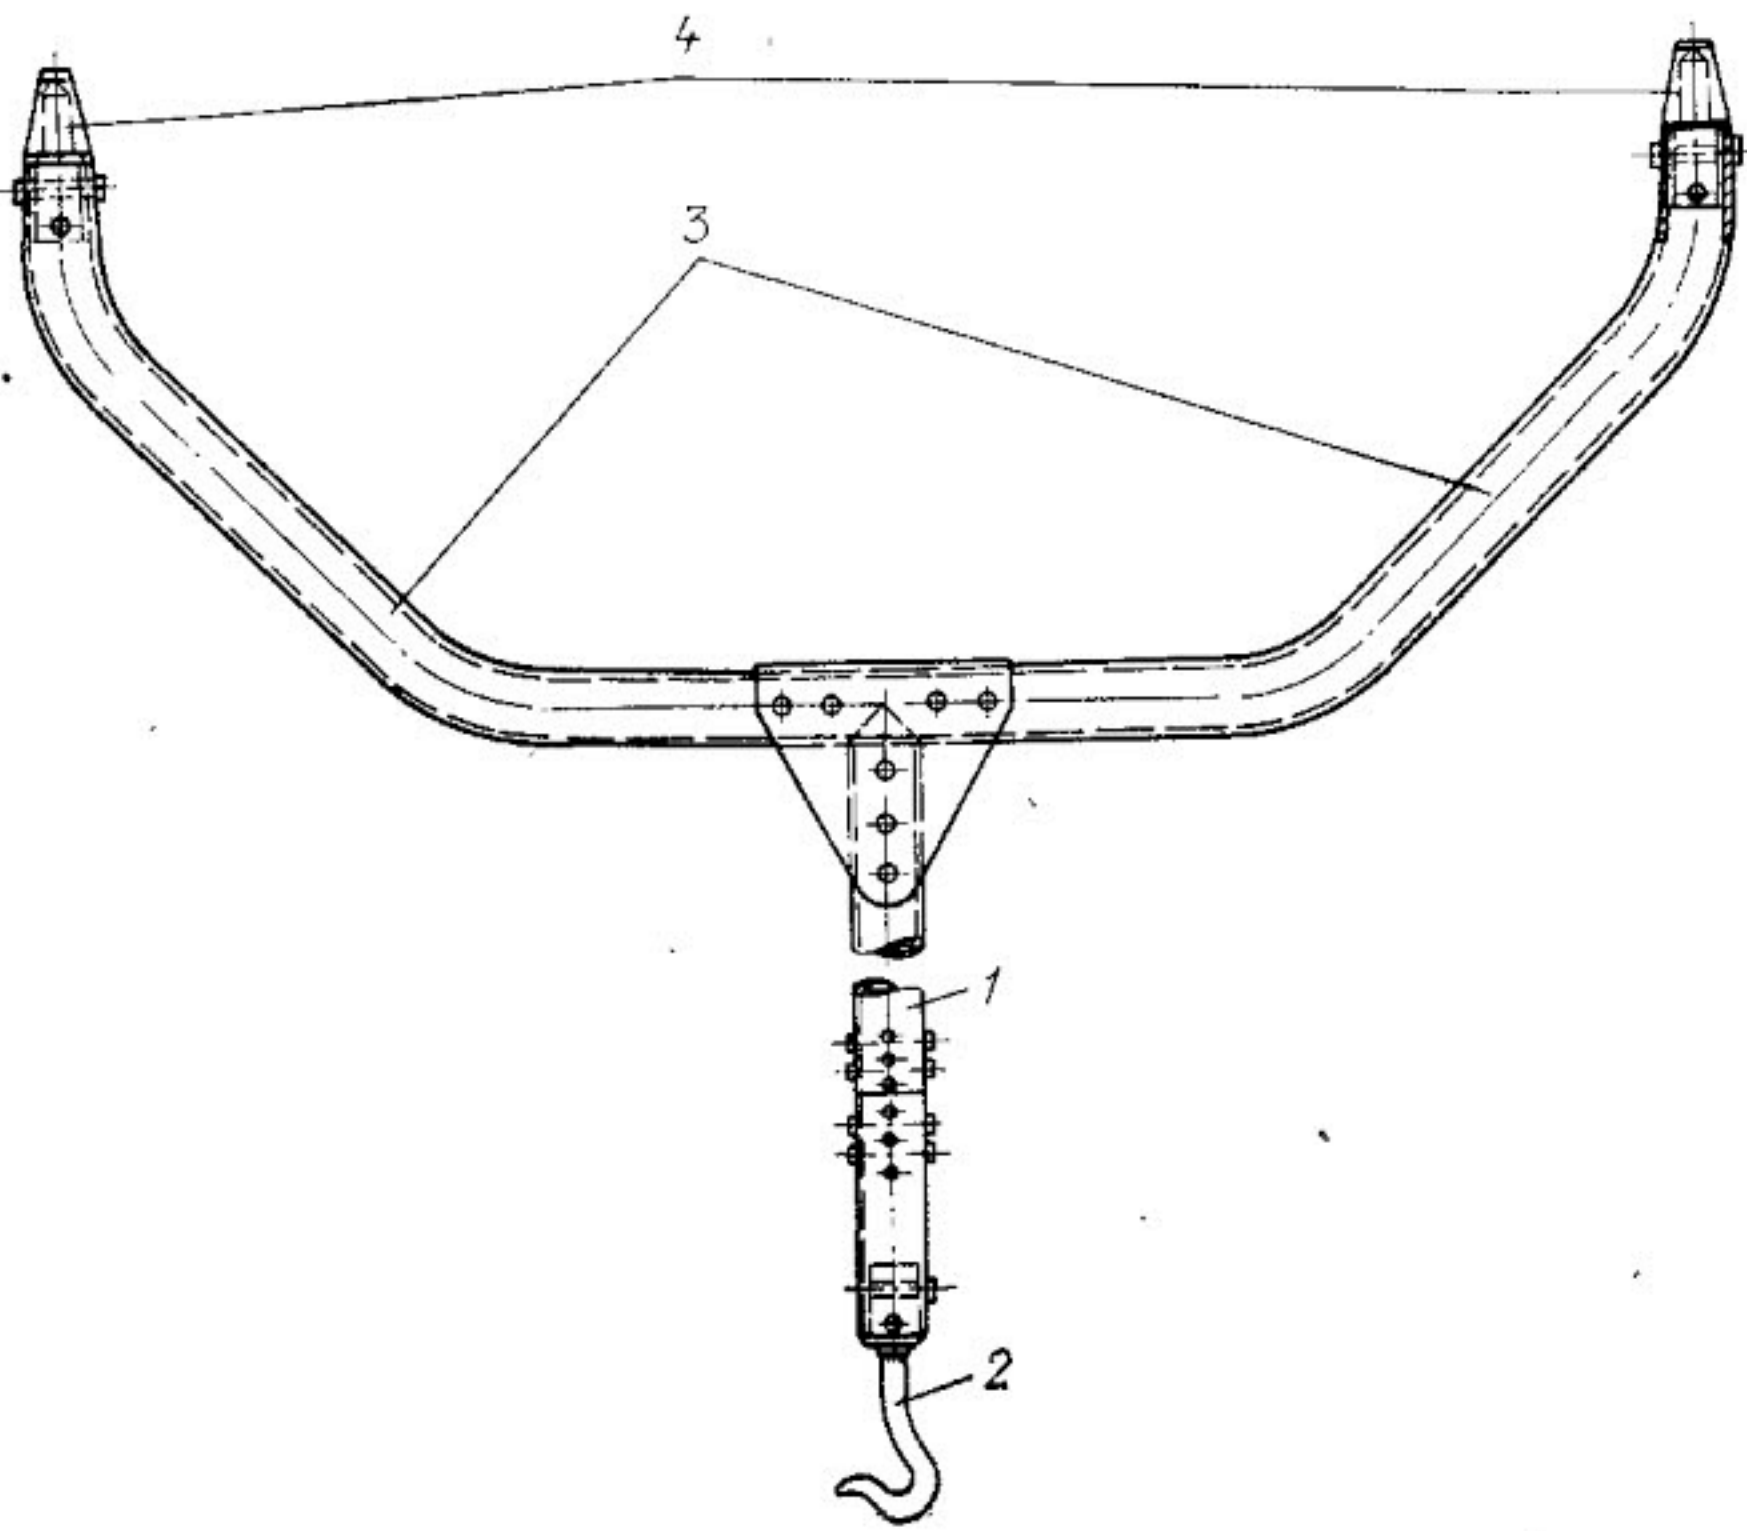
Вилка для надевания чехла на лопасть: 1—рукоятка; 2—крюк; 3—рожки; 4—наконечники
